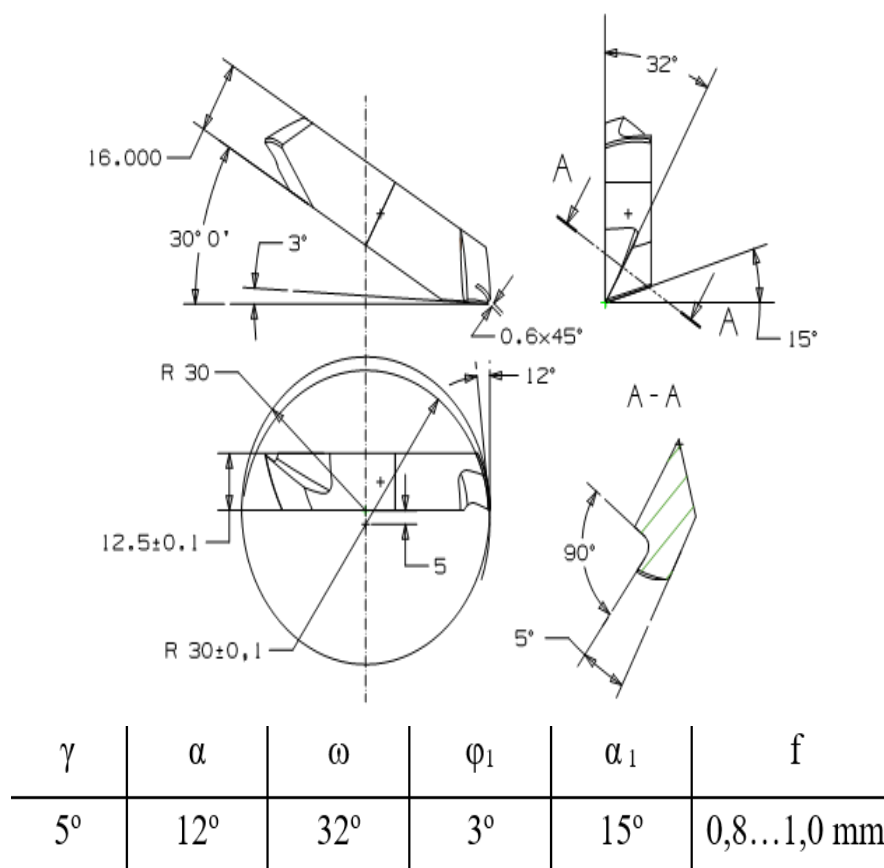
Лабораторные фрезы из быстрорежущей стали.
